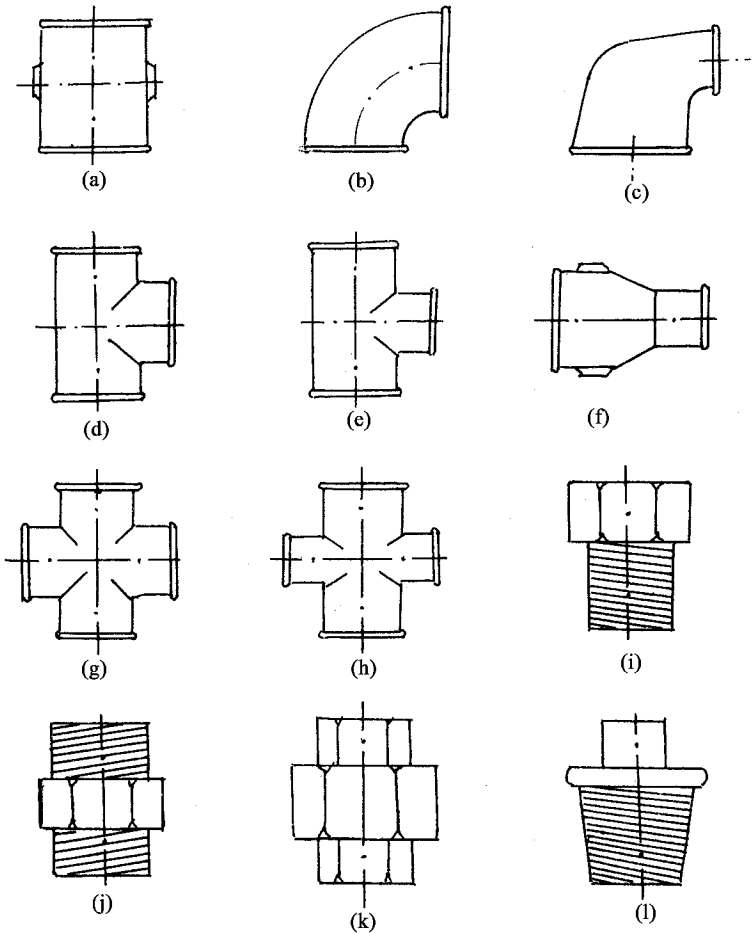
低压流体输送用焊接钢管的管件
